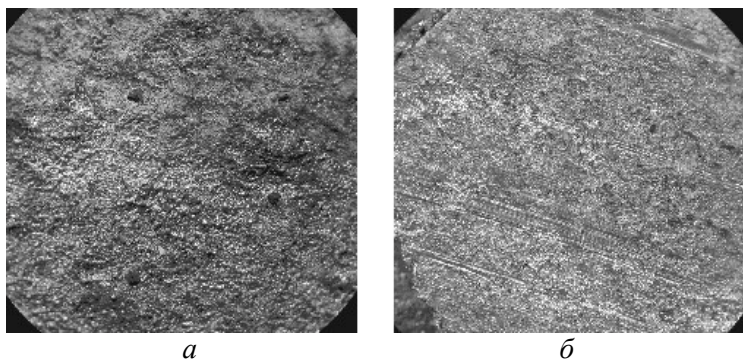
Поверхня композитів після обробки: а – з впорядкованими алмазами; б– з хаотично розташованими алмазами
